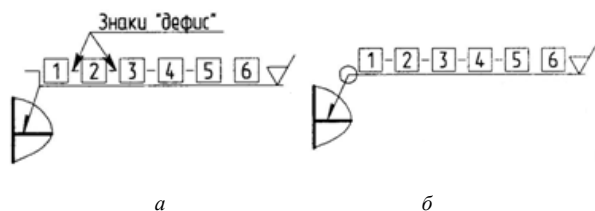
Схема обозначения стандартного сварного шва:
